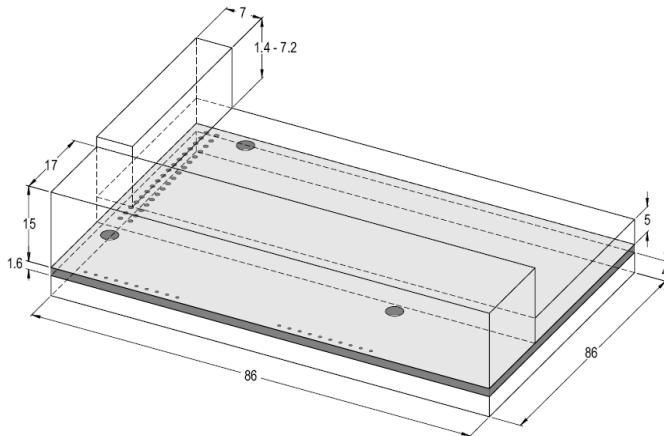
EC-TX103 通信卡外形尺寸 (单位: mm)
